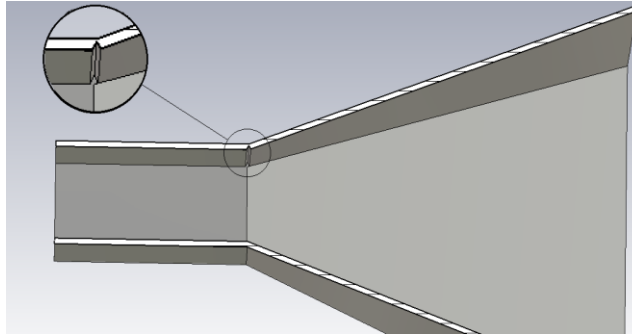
Модель рупора в сечении с нарушением сварного шва на стыке волновода с раскрывом.
